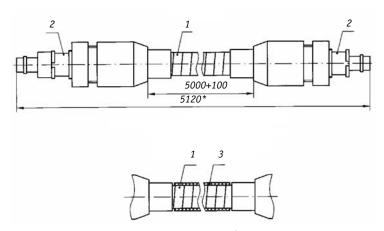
Жгут соединительный ИЦФР.685661.015: 1 – металлорукав; 2 – розетка 2РМ14КУ34Г1В1В; 3 – трубка термоусадочная
